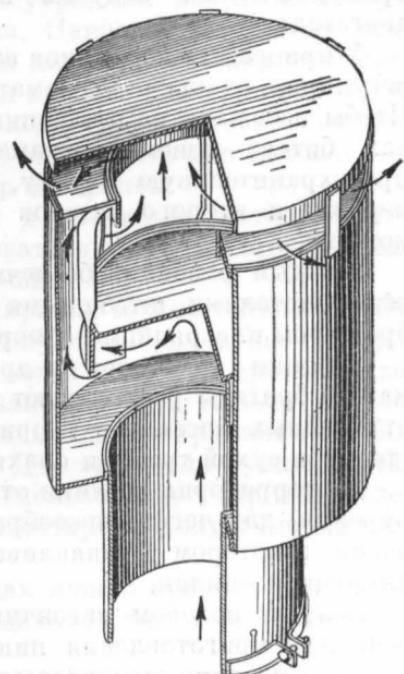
Искрогаситель для локомобилей конструкции тов. Демченко.
